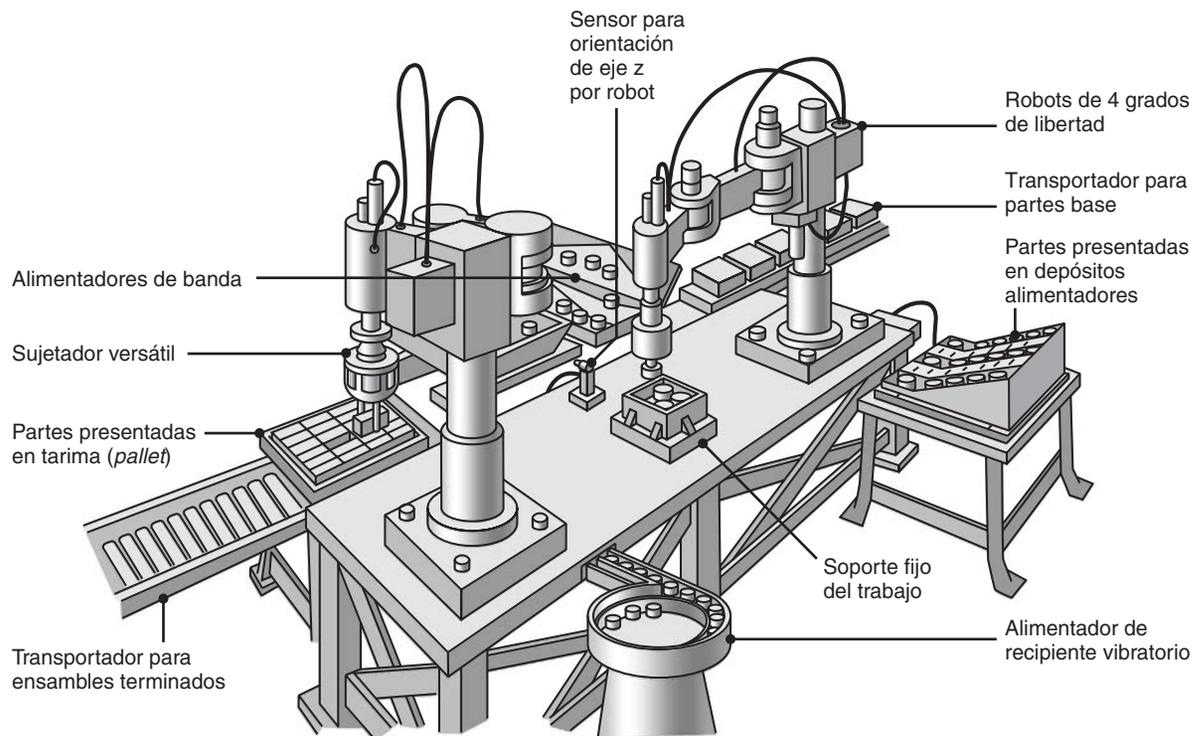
Estación de ensamblaje de robot de dos brazos. Fuente: *Product Design for Assembly*, edición de 1989, de G. Boothroyd y P. Dewhurst. Reproducida con permiso.
